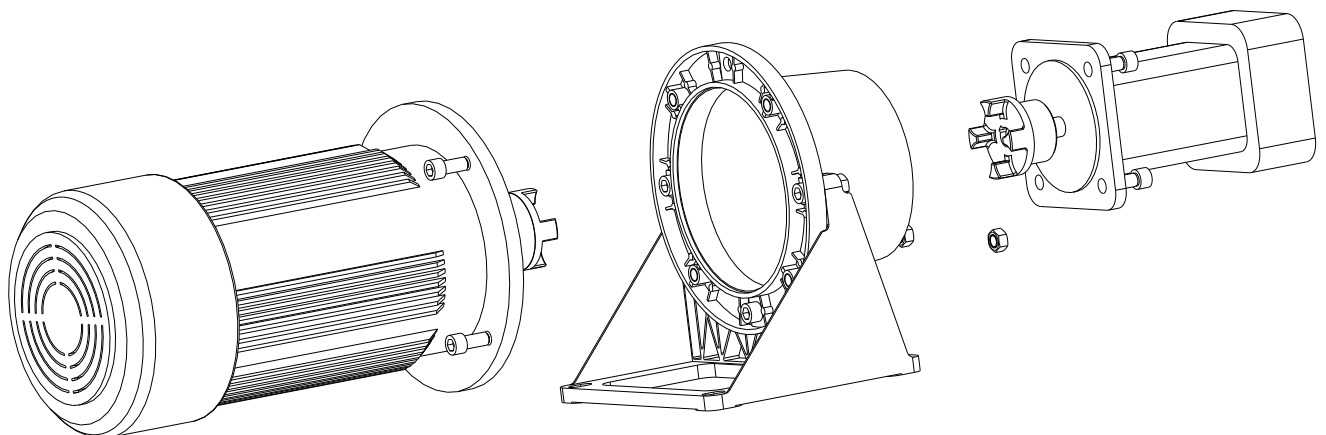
Montage E-Motor bzw. Pumpe mit Pumpenträger und Fußflansch
